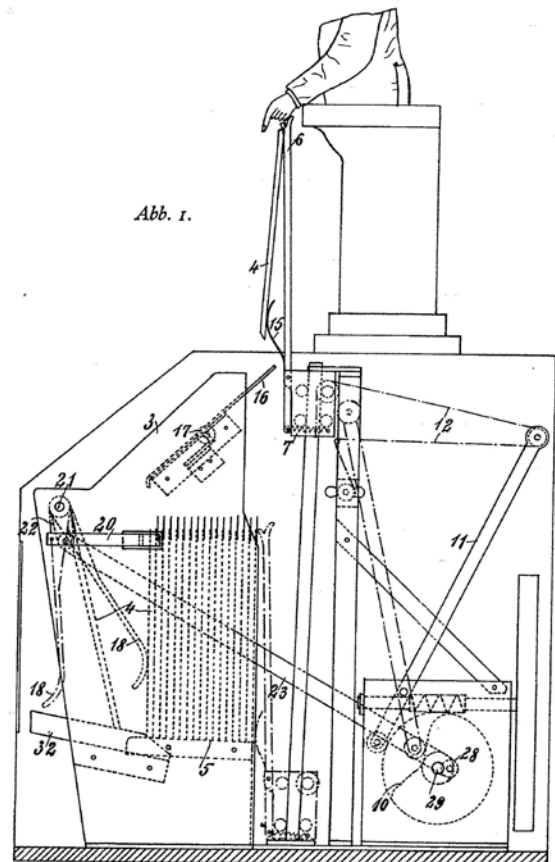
Patentzeichnung der Hebe- und Abfedermechanik der Reklamemaschine
